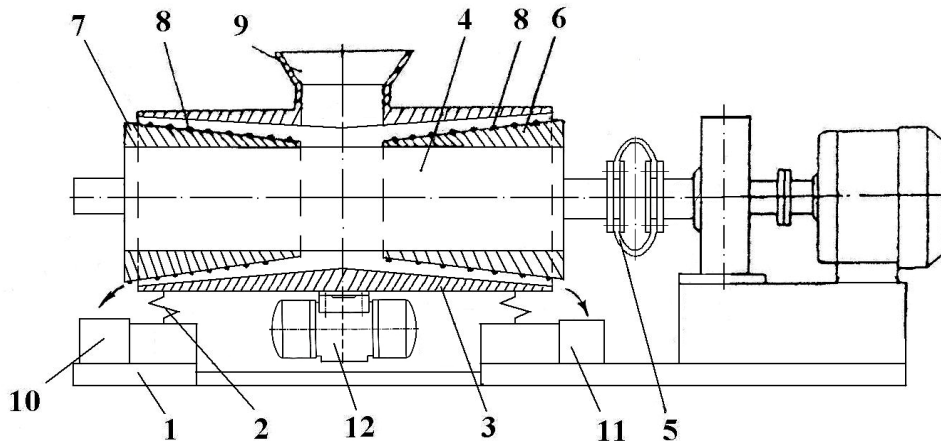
Конструктивная схема внутривалковой конусной мельницы
